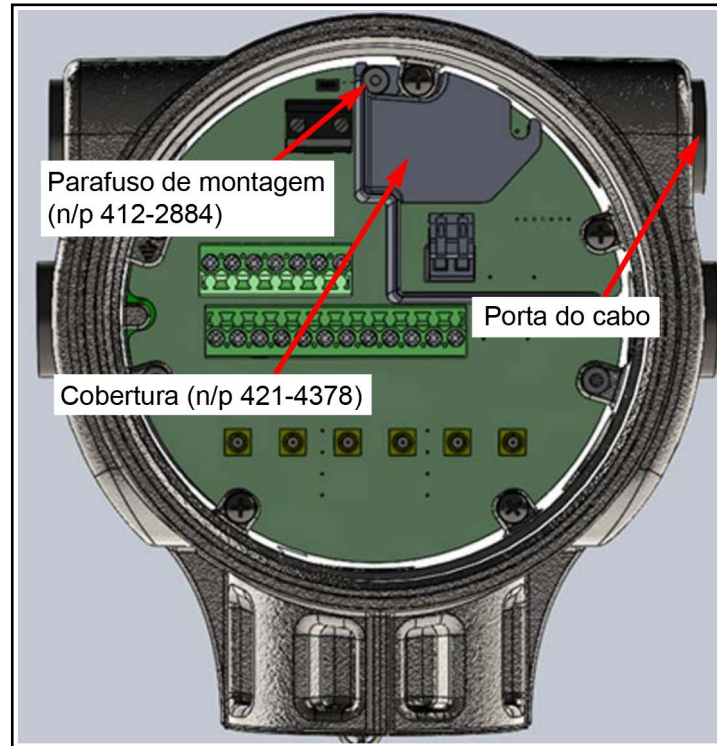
Cobertura de FISCO instalada e parafusos de montagem
